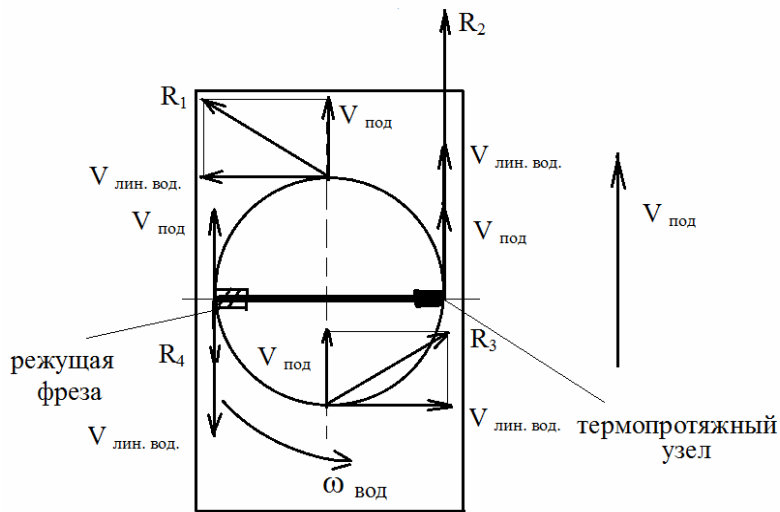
Кинематическая схема привода калибровально-шлифовального механизма с поступательно-вращательным движением:
